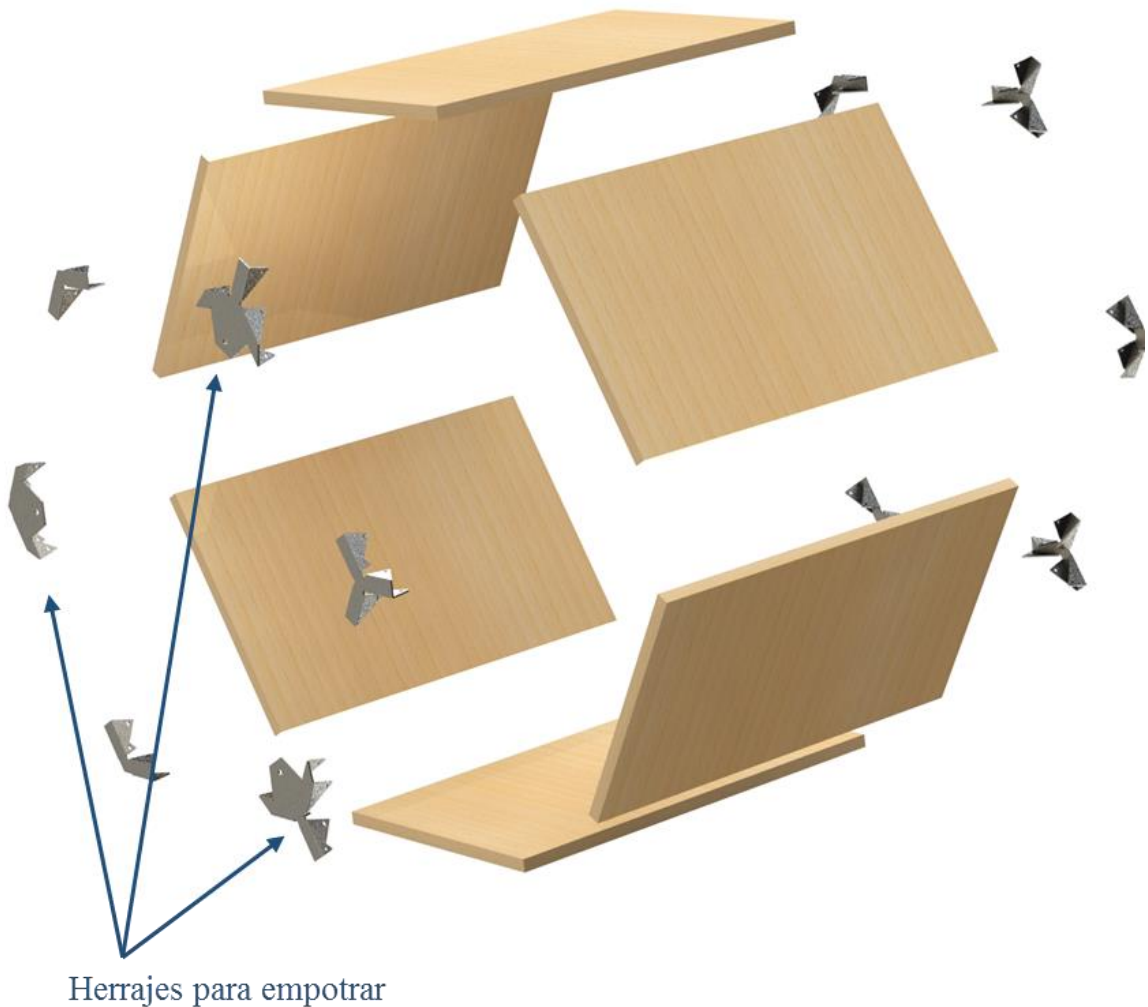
Vista explosionada del ensamblaje de un hexágono base con herrajes de acero
